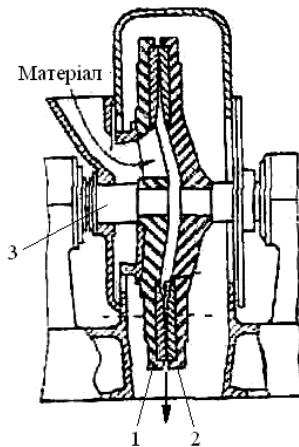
Схема дискової дробарки: 1, 2 – диски; 3 – горизонтальний вал
